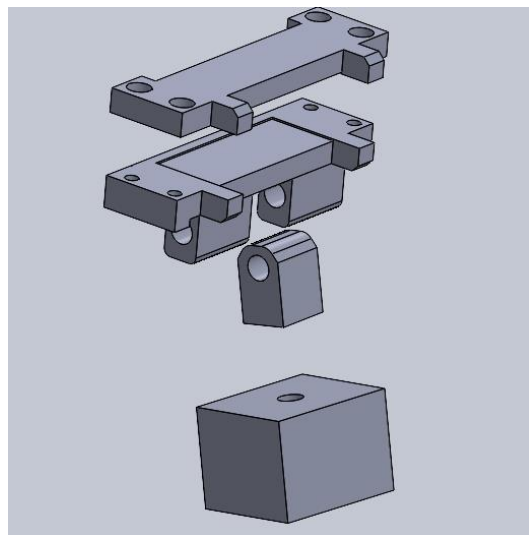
Diseño de la estructura pendular diseñada en SolidWorks
